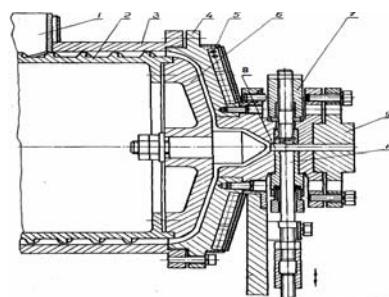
Червячно-дисковый экструдер: 1 – бункер; 2 – диск; 3 – корпус; 4 – неподвижный диск; 5 – нагреватель; 6 – подвижный диск; 7 – термопара; 8 – выходное отверстие; 9 – формующая головка; 10 – датчик давления
